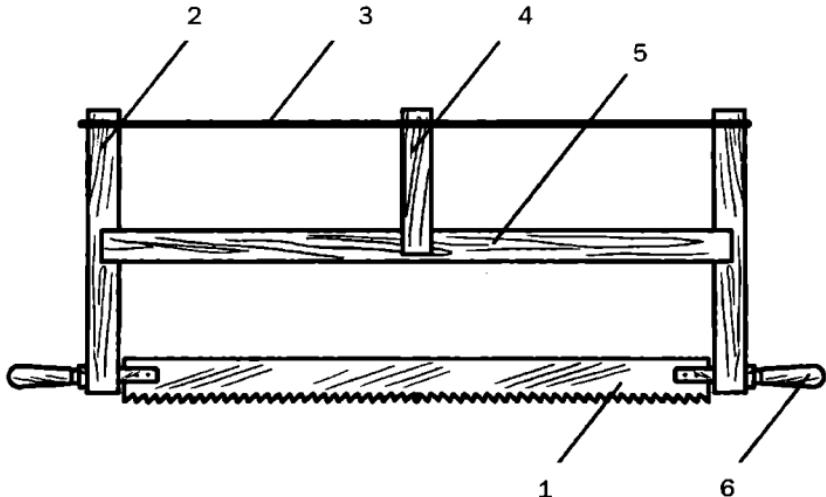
Лучковая пила: 1 — пильное полотно; 2 — стойки; 3 — тетива; 4 — закрутка; 5 — распорка; 6 — ручка
